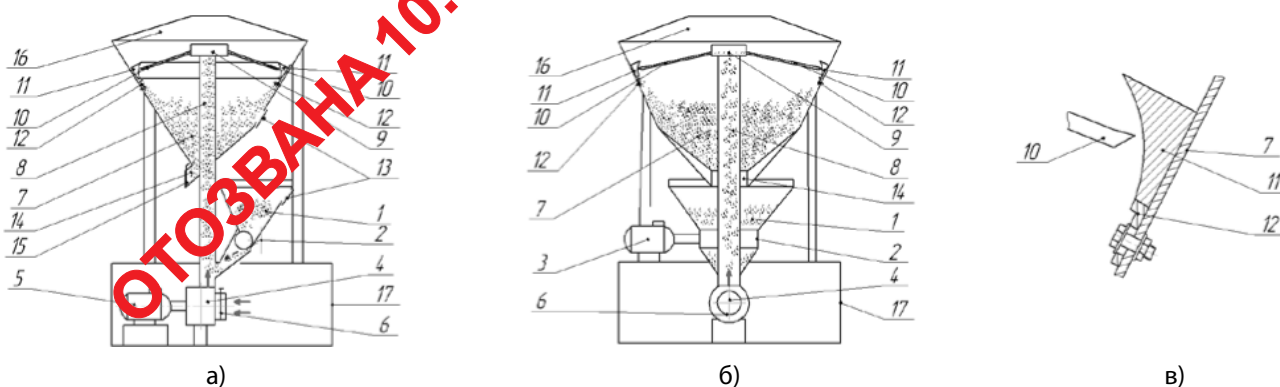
Пневматический скарификатор: а) – общий вид с приводом на вентилятор; б) – общий вид с приводом на катушечный с инжектором дозатор; в) – регулируемая опора цилиндрической наждачной поверхности; 1 – загрузочный бункер; 2 – катушечный с инжектором дозатор; 3 – мотор-редуктор; 4 – вентилятор; 5 – электродвигатель; 6 – жалюзийная заслонка; 7 – бункер скарифицированных семян; 8 – шахтная труба; 9 – распределительная головка; 10 – семяпроводы; 11 – наждачная поверхность; 12 – опоры; 13 – смотровые окна; 14 – выгрузное окно; 15 – заслонка; 16 – матерчатая крышка; 17 – рама
